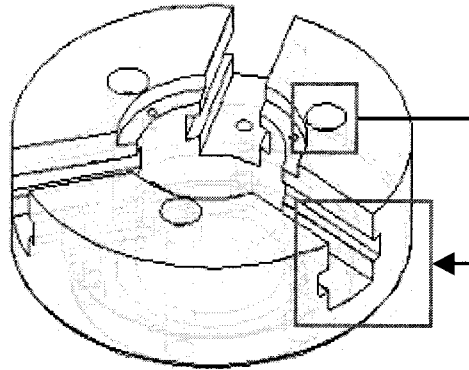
Fixturing을 고려한 가공선행관계의 예 (Chuck Body)
